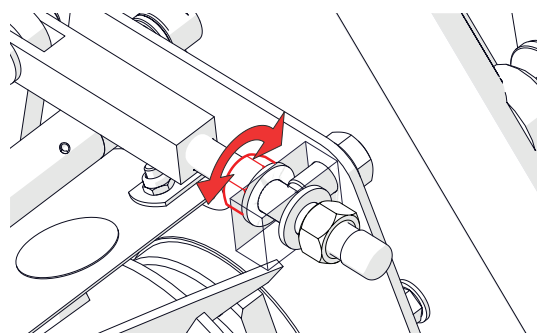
D - Serrer/Desserrer l'écrou de réglage.
